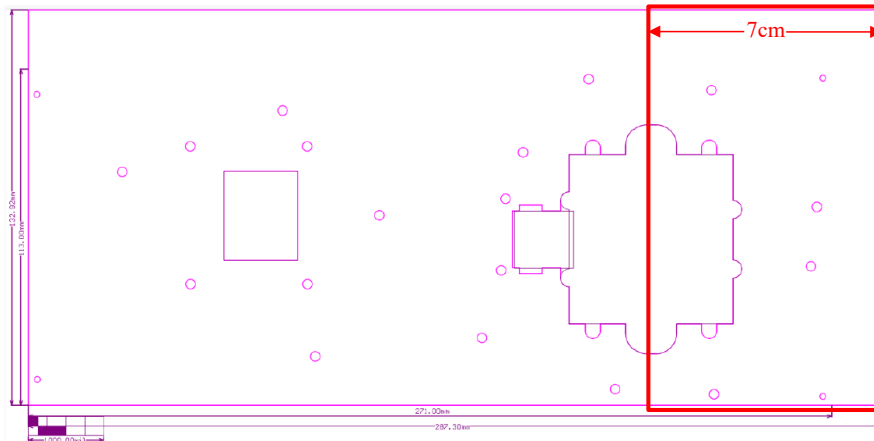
Porzione di PCB che è possibile rimuovere per ridurre le dimensioni
